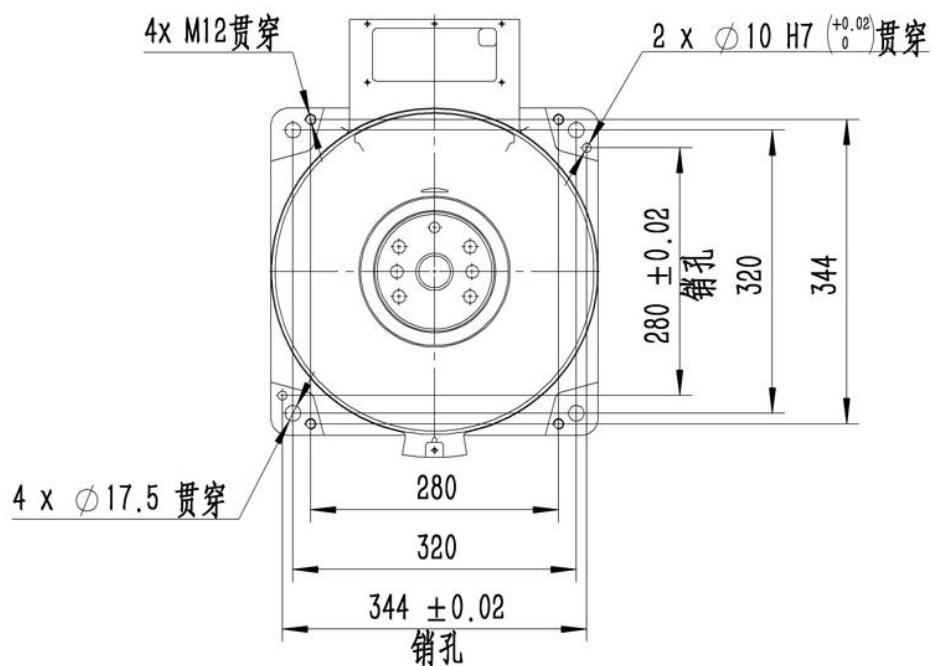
机器人底座安装尺寸 Diagram 2.9 Installation dimension for robot pedestal
